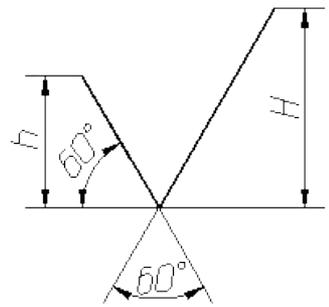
Обозначение шероховатости поверхности без указания способа обработки
